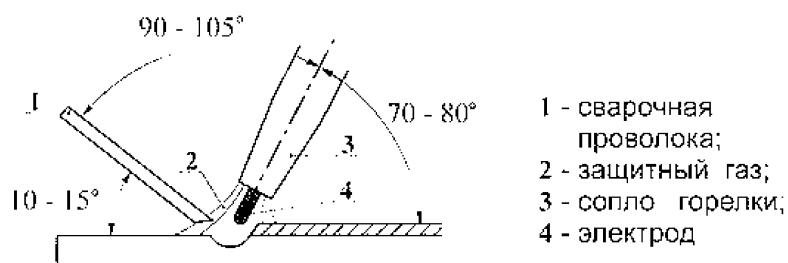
Схема расположения горелки и сварочной проволоки при ручной аргонодуговой сварке
